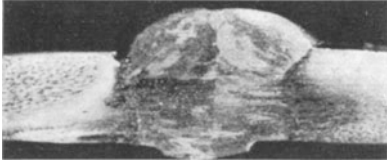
Schliffbild einer Aluminiumblechschweißnaht.
